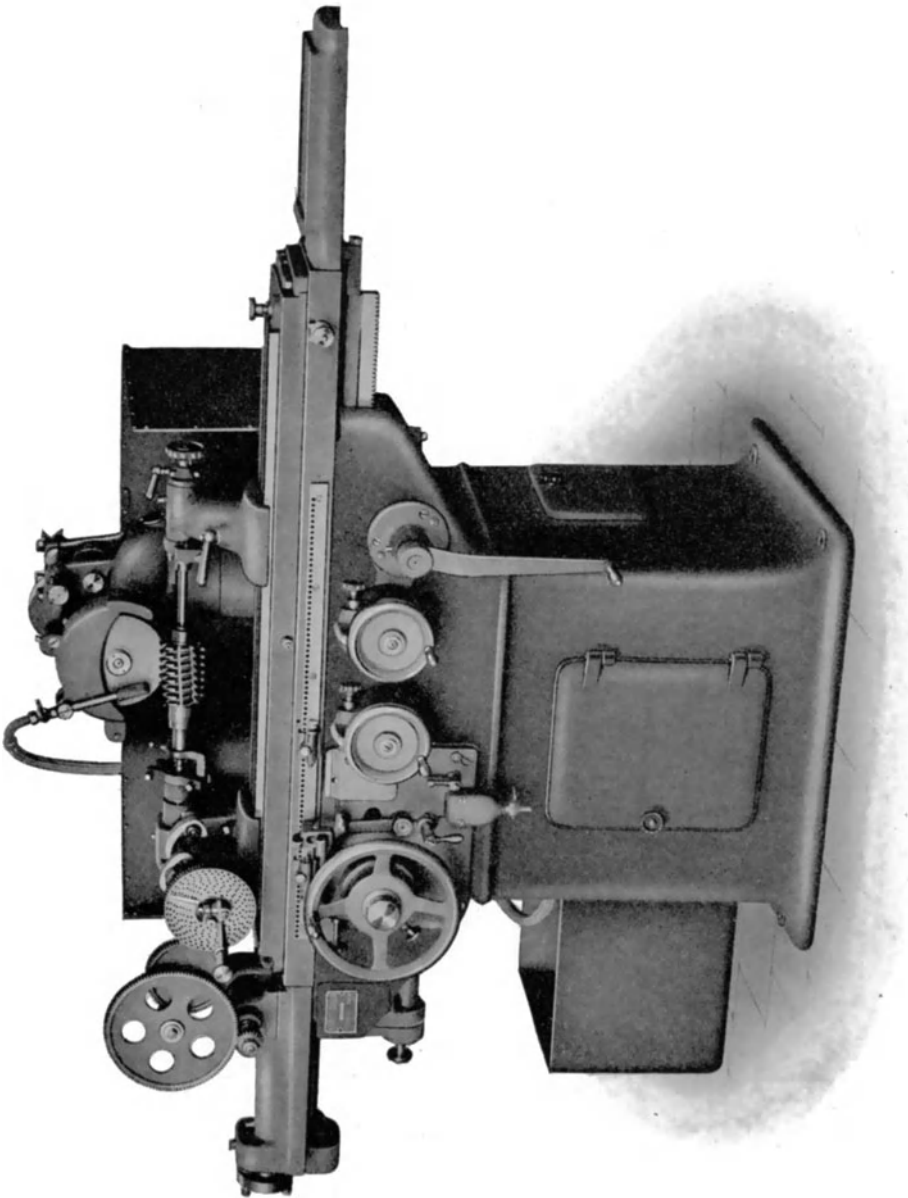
Die Universal-Werkzeug-Schleifmaschine der Naxos-Union.
